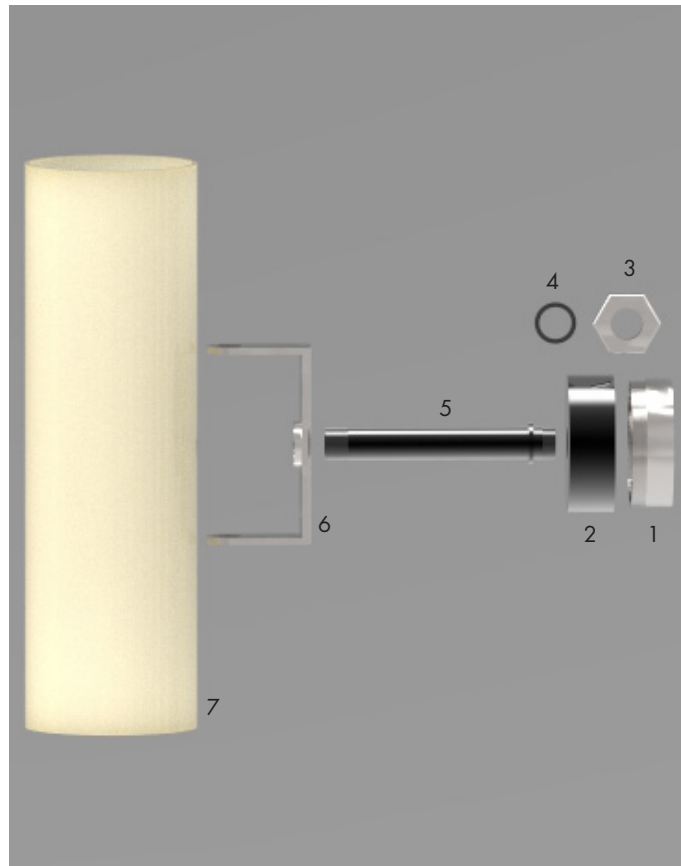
Representação em 3D da vista explodida do aplique de parede
